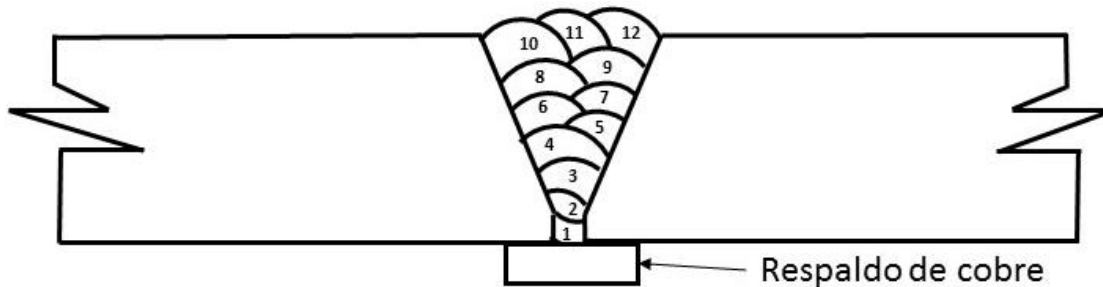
Esquema de la soldadura multipasos en cupón
